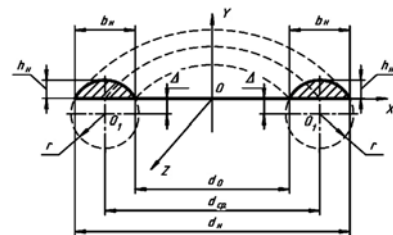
Схематичное представление диаметрального сечения напльвов металла и форма образуемой ими поверхности по краю лунки
